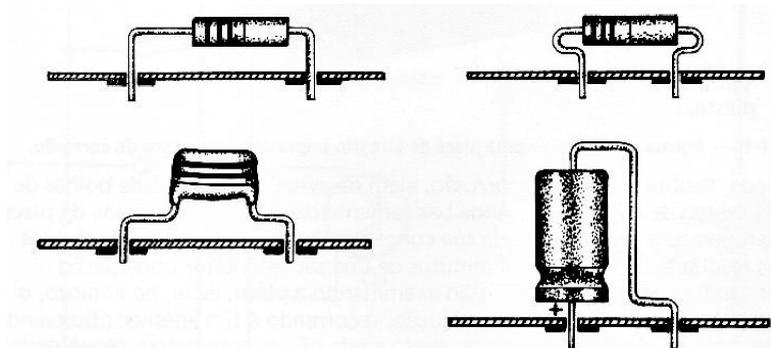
Artíficos para a soldadura de componentes cujas extremidades dos lides não coincidam com a furação realizada na plaqueta de circuito impresso.
